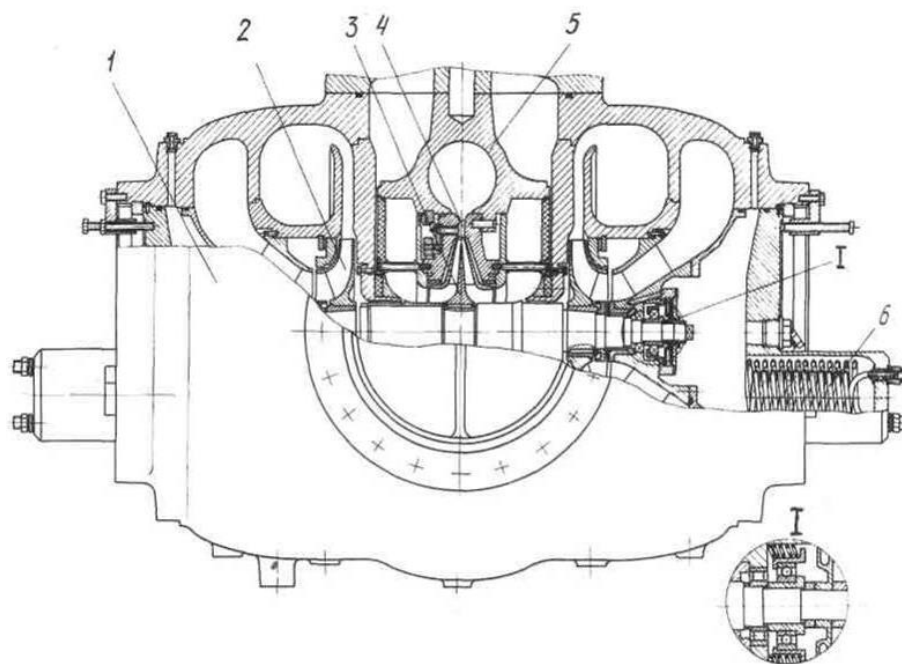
Двухпоточный (две параллельно работающие проточные части) турбодетандерный агрегат для охлаждения газа: 1 – корпус
